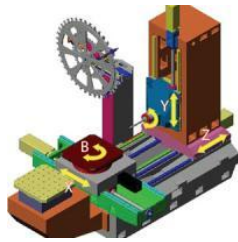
Схема устройства смены инструмента путем относительного перемещения шпинделя: станок горизонтальный сверлильно-фрезерно-расточной с ЧПУ модели 630Н ОАО «Стерлитамакский станкозавод»
